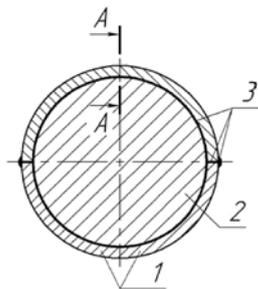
Схема клеевого соединения при восстановлении наружной цилиндрической поверхности детали в поперечном сечении
